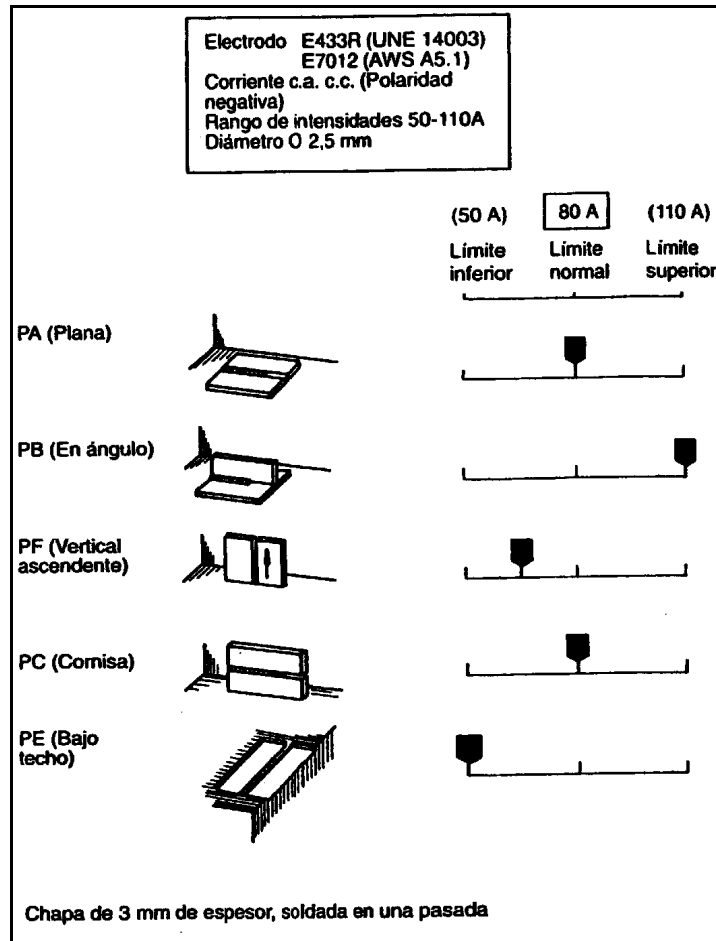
INTENSIDAD DE SOLDADURA EN FUNCIÓN DE LA POSICIÓN
